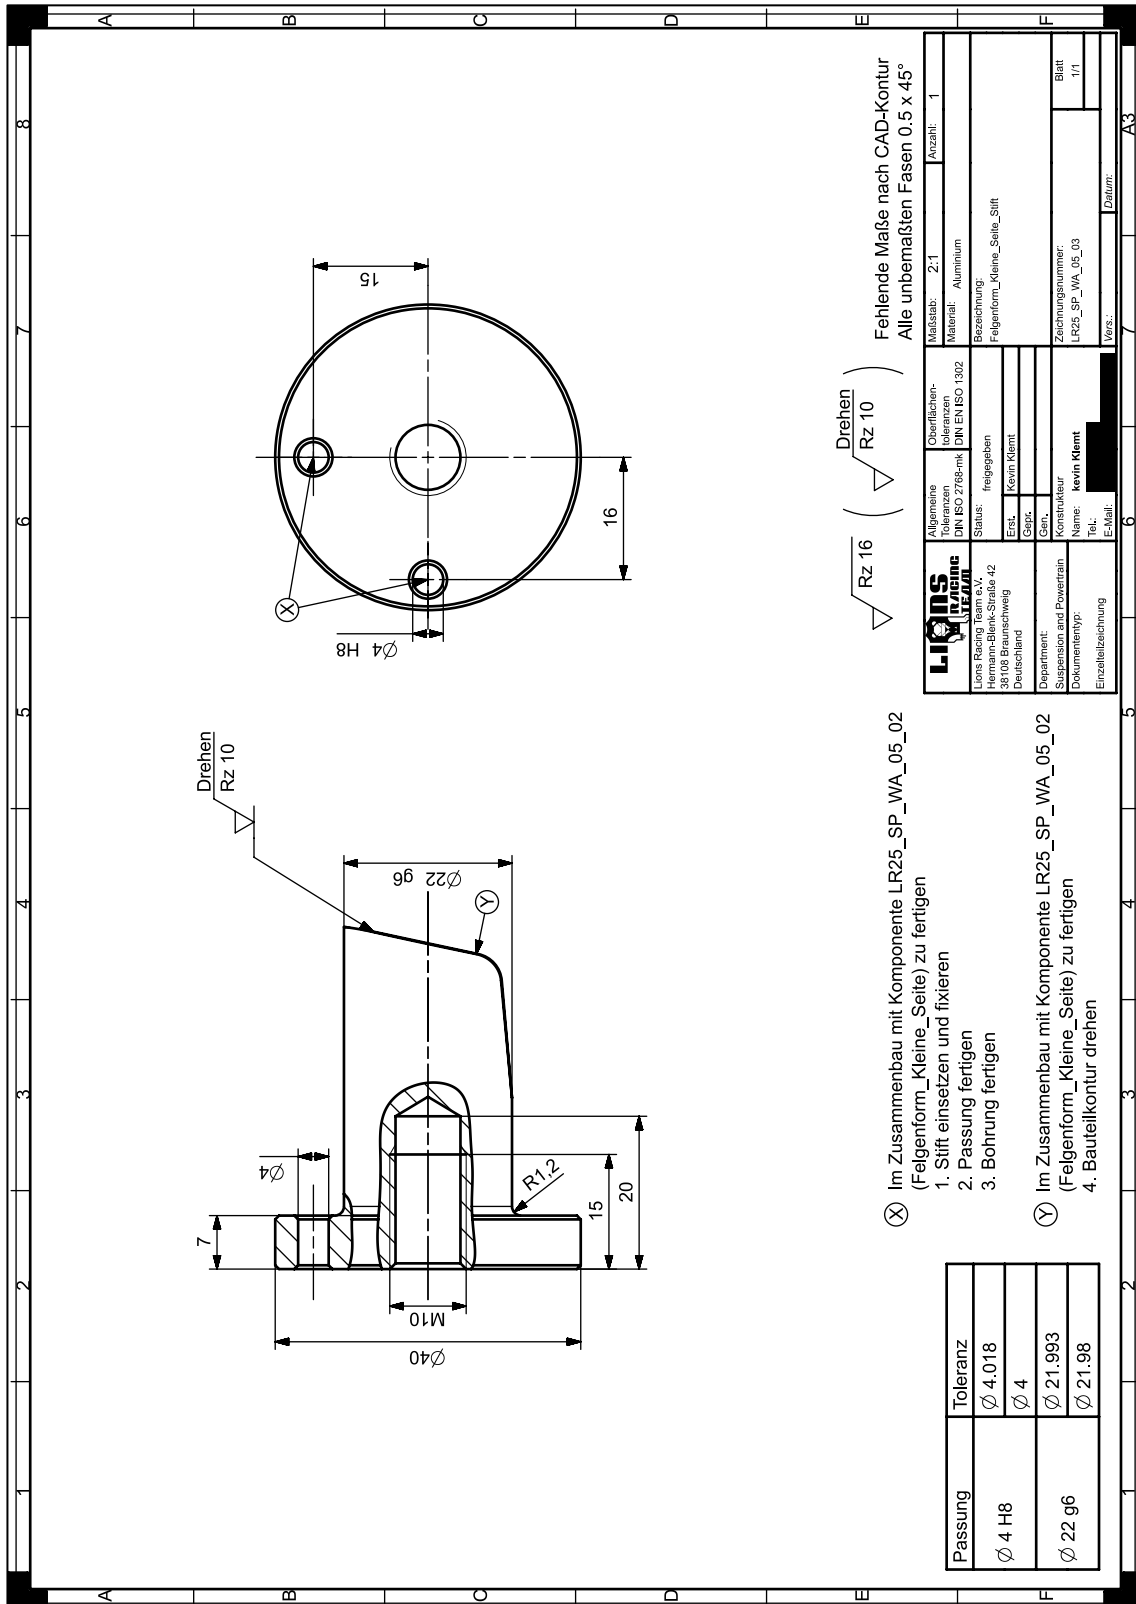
Technische Zeichnung Felgenform (3/4); Stift [42]
